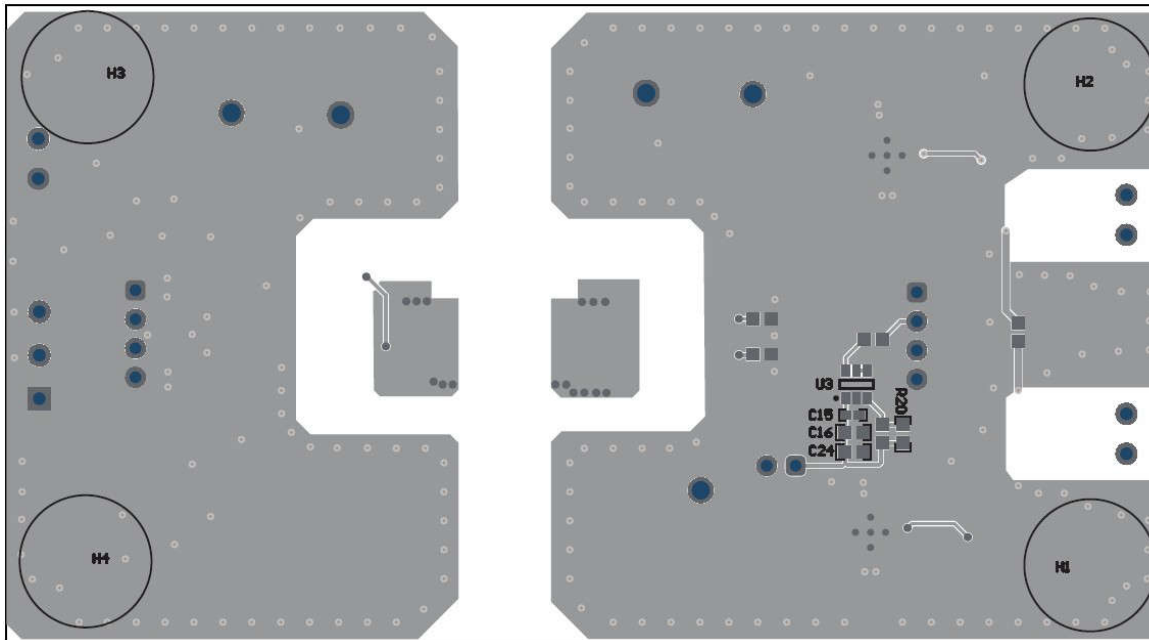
ISOW1050DWEEVM PCB 布局 - 底层
